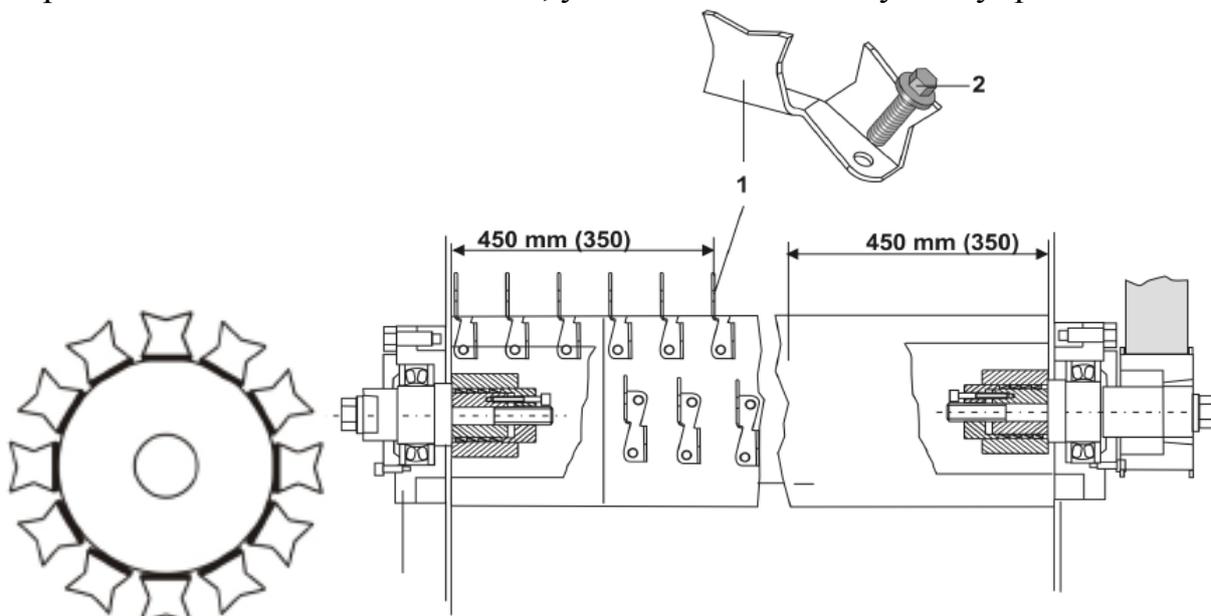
Конструкция ножевого барабана кипоразрыхлителей Unifloc А11
